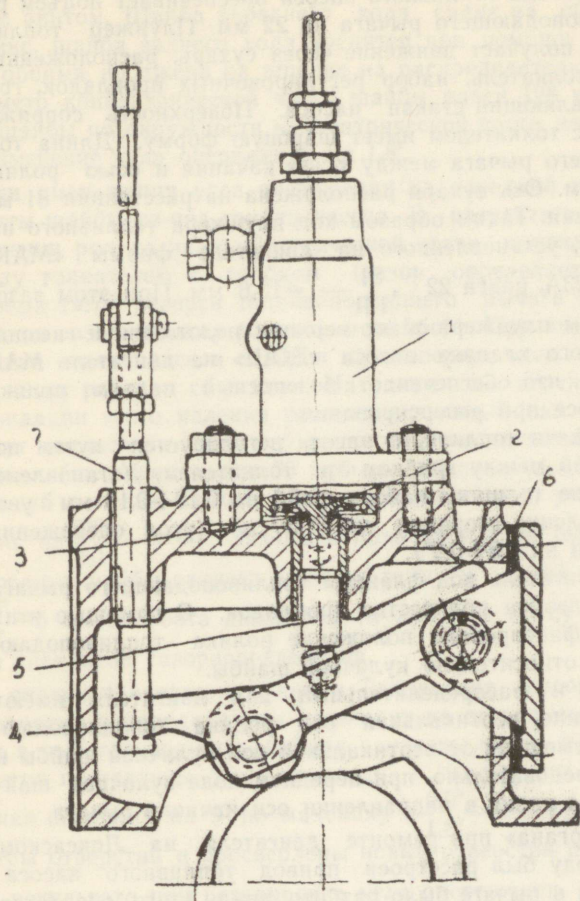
Общий вид привода и топливного насоса двигателя МАК
